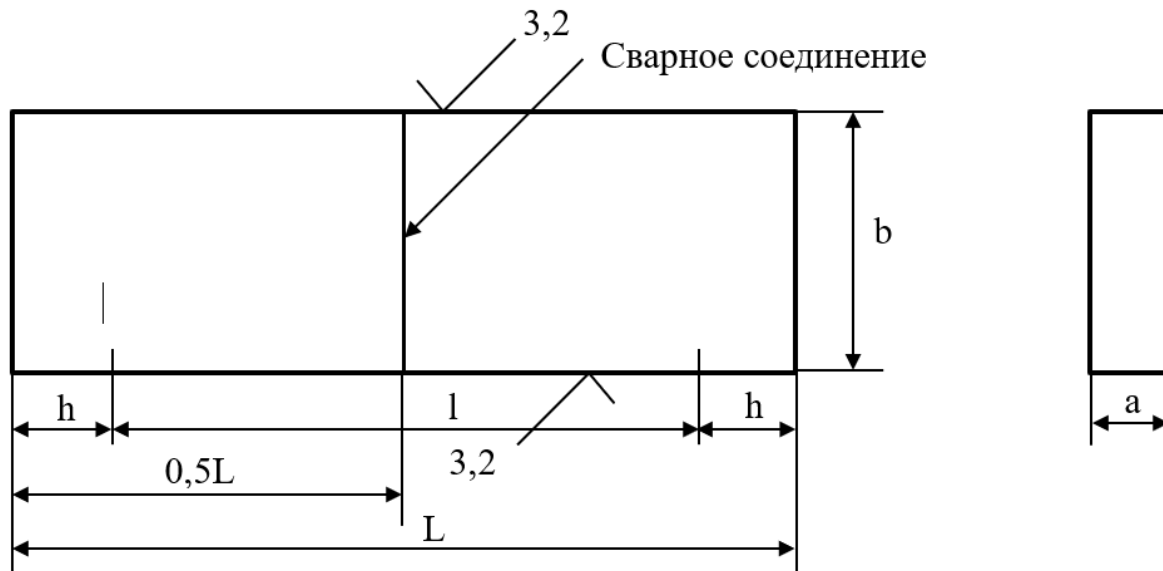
Образцы для испытаний контрольных сварных соединений по ГОСТ 6996
